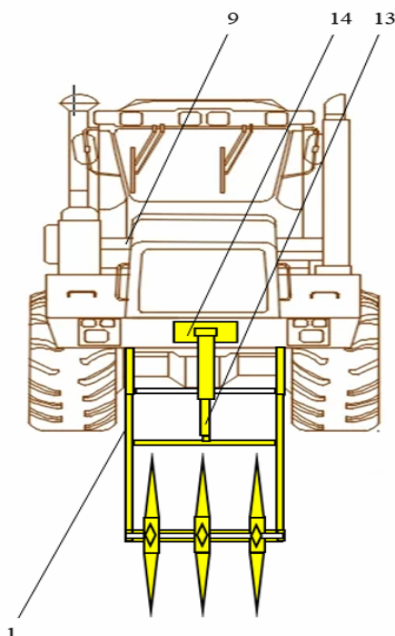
Фронтальный вид колёсного полурамного трактора с установленным фронтальным прокальвателем-щелерезом
